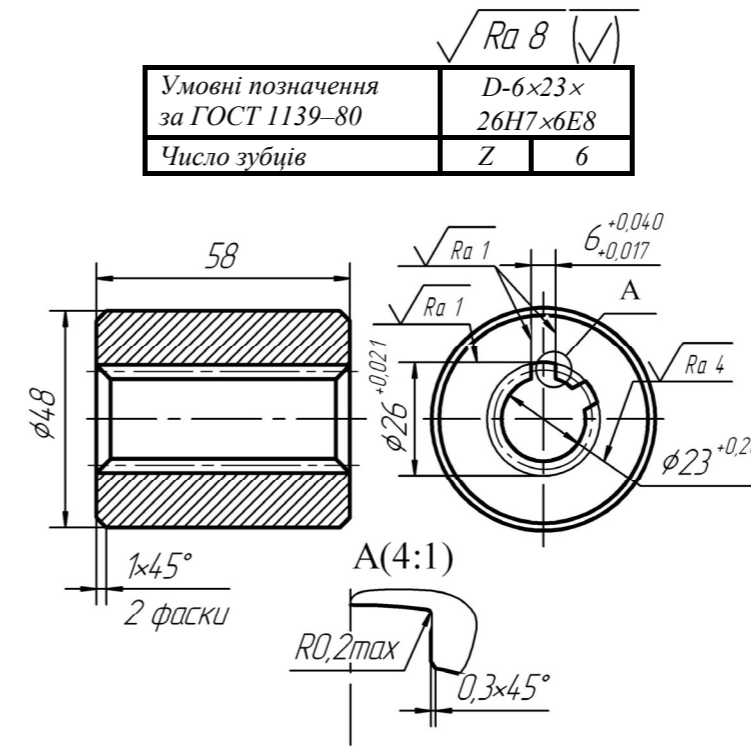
Приклад оформлення робочого кресленика шліцьової муфти
